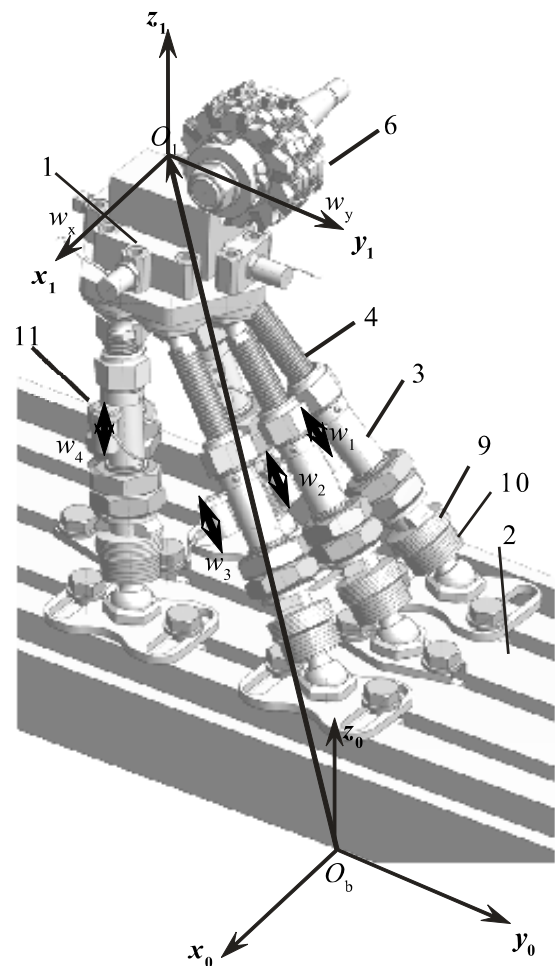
Стенд для дослідження динамічної похибки просторового механізму
